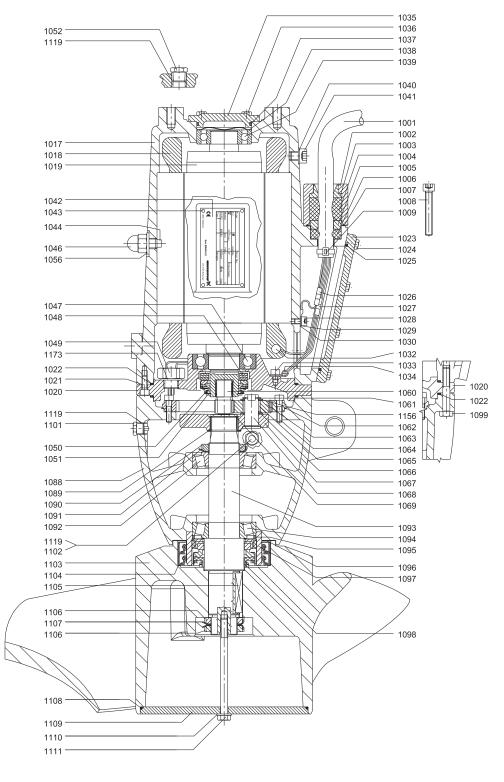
Чертёж в разрезе, SRP.35.50.xxx, SRP.50.50.xxx
